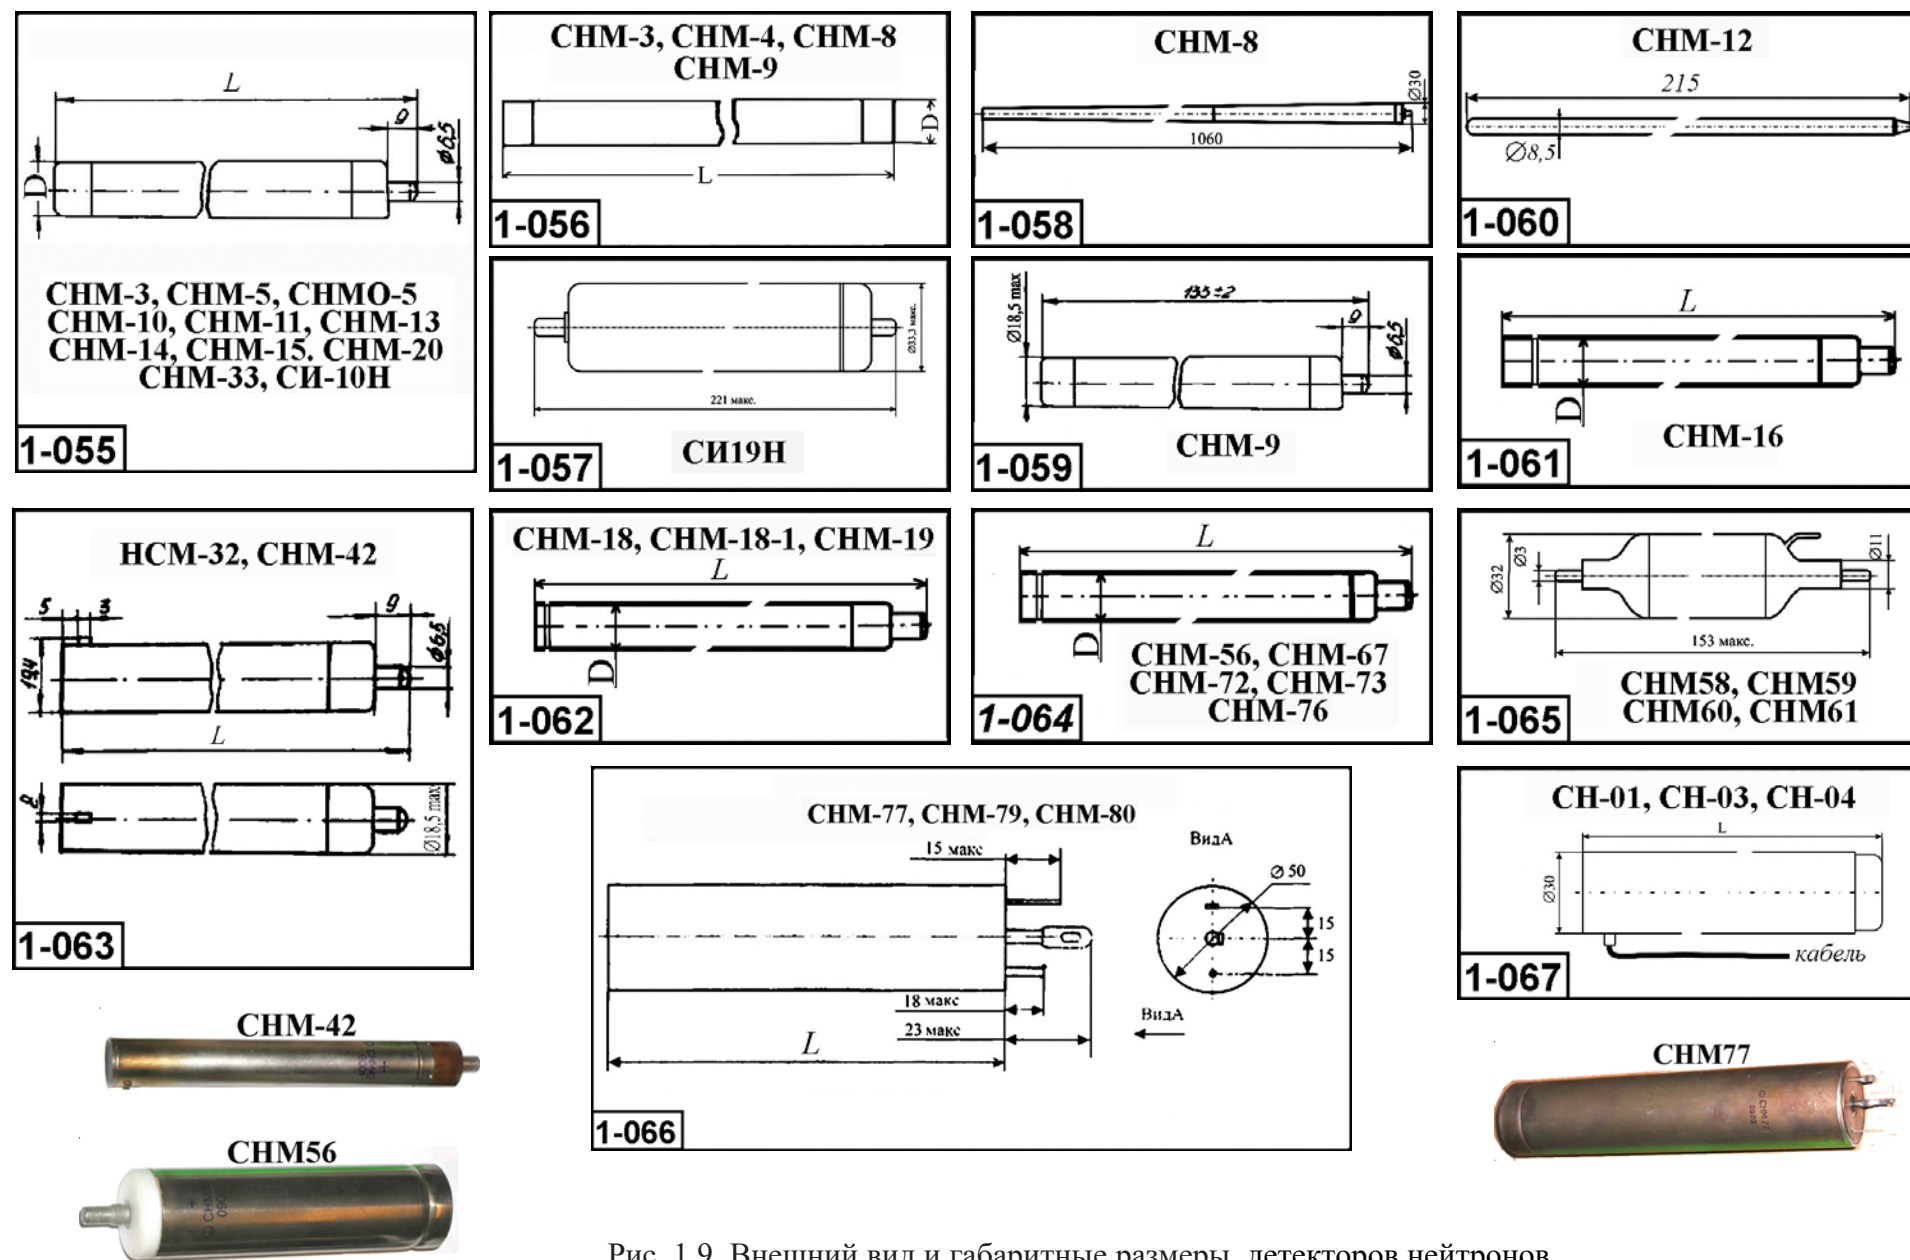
Внешний вид и габаритные размеры детекторов нейтронов
